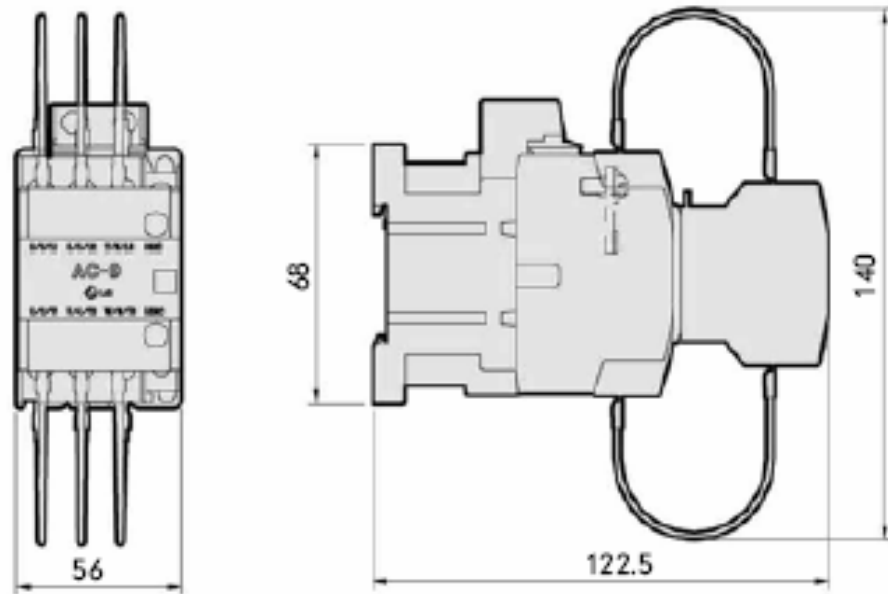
Dimensiones Contactor LS serie GMC-9
